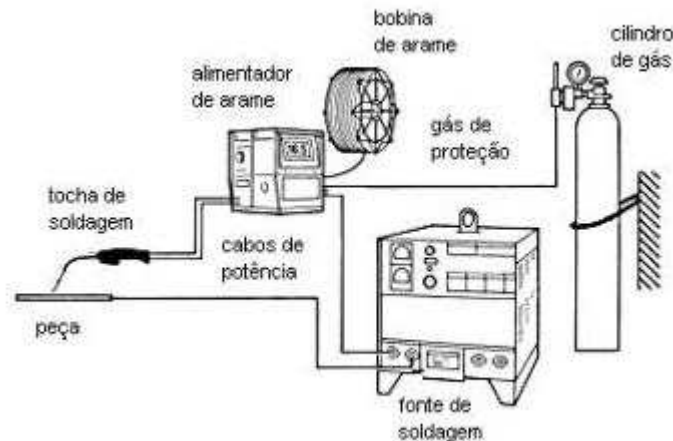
PROCESSO BÁSICO DE SOLDAGEM MIG/MAG - Fonte: Vieira (2012)
